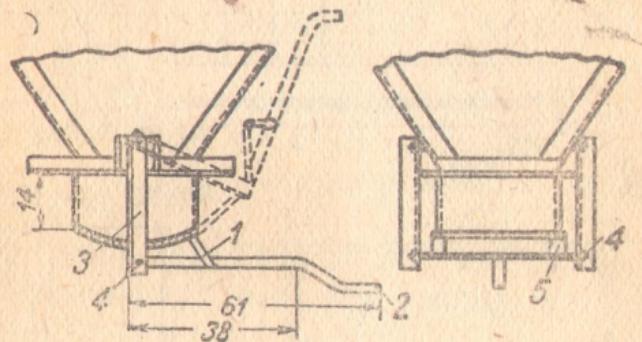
Секторный затвор бункера с удлиненной рукояткой: 1—лапка; 2—рычаг; 3—угольники; 4—болтовой стержень; 5—уголки жесткости
